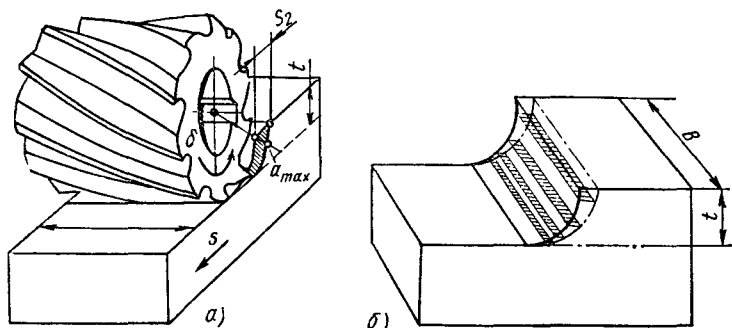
Фреза и заготовка в рабочем состоянии (а) и изменение площадки поперечного сечения среза (б) вдоль дуги контакта (у прямозубой фрезы)
